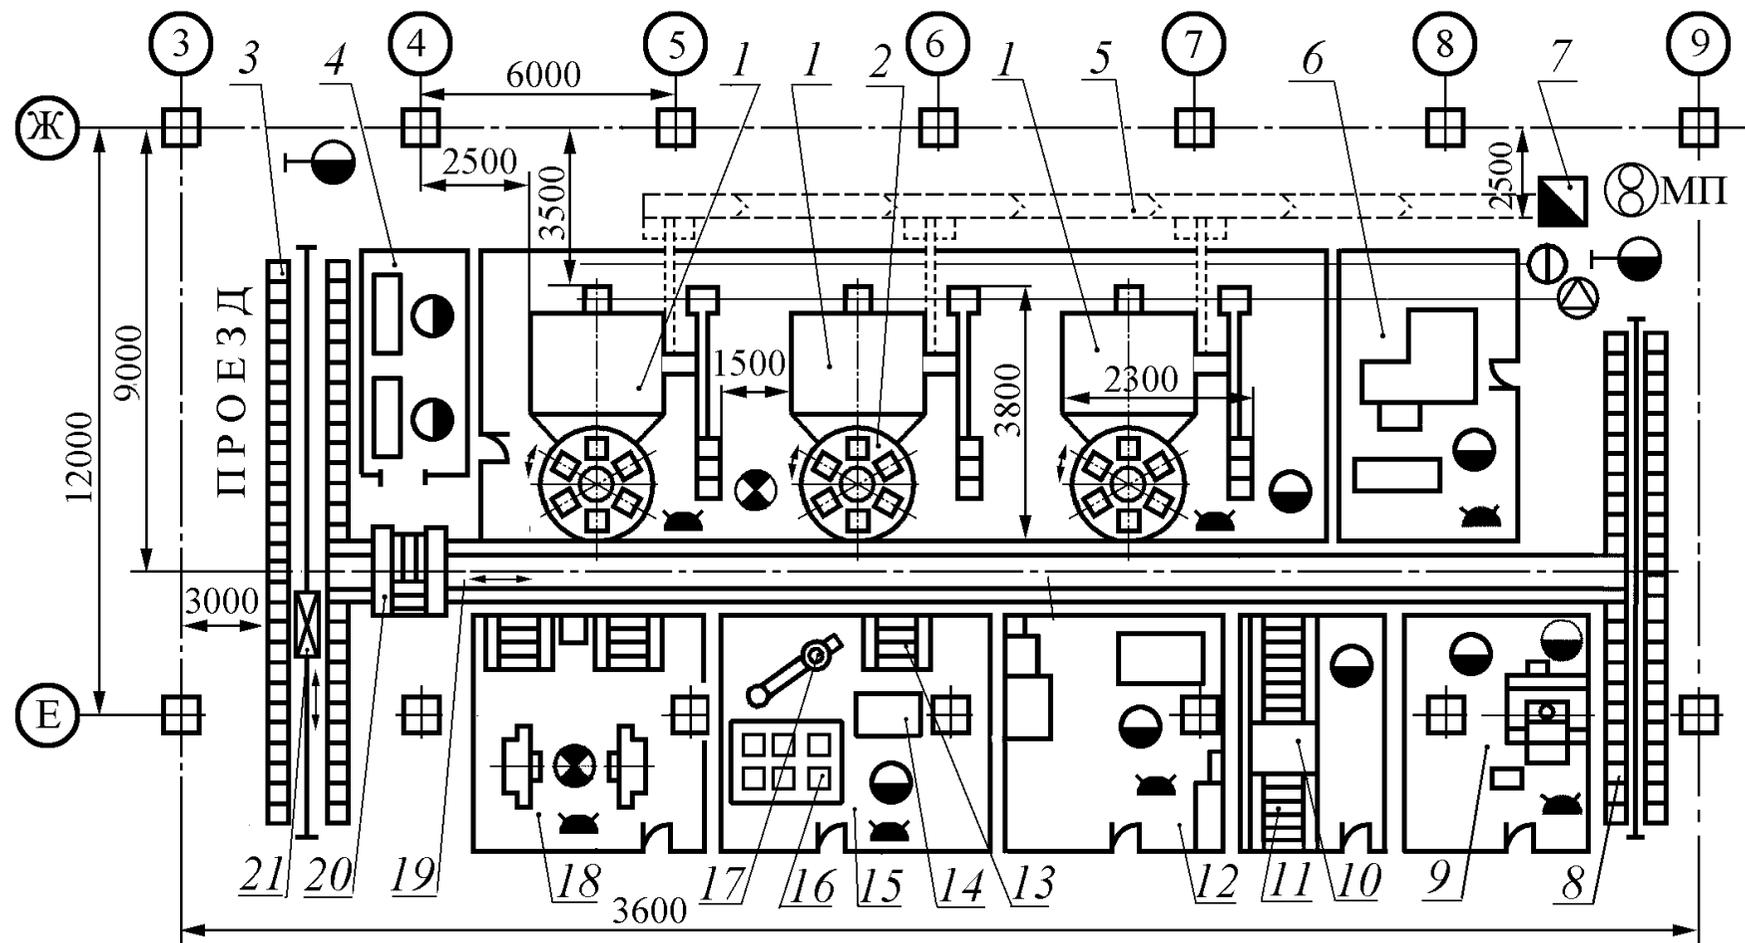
П14. ГПУ для обработки корпусных деталей с АТСС Т-образной компоновки:
